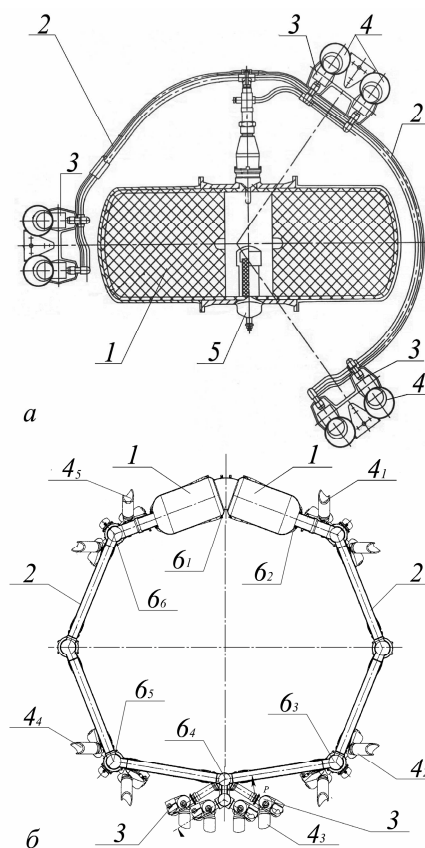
Примеры конструктивных схем двигательных установок: 1 – твердотопливный газогенератор; 2 – газоходы; 3 – регуляторы расхода и привод; 4, 4₁–4₅ – сопловые блоки; 5 – воспламенительное устройство, 6₁–6₅ – контрольные сечения
